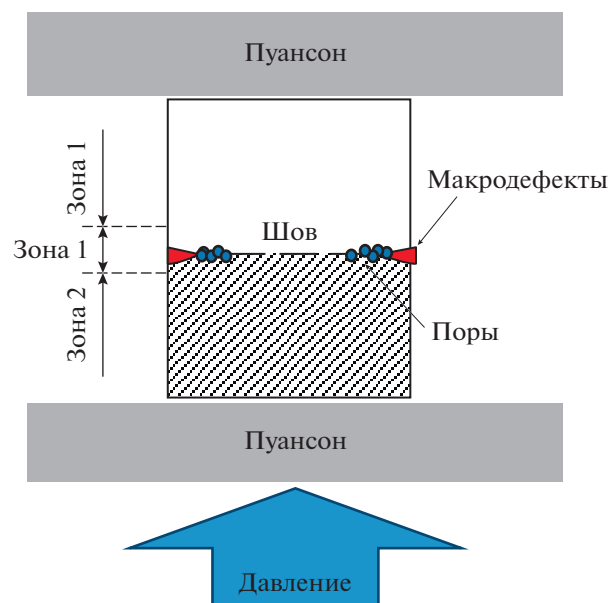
Схема диффузионной сварки образцов с помощью ЭИПС и расположение различных зон в исследуемых образцах.
